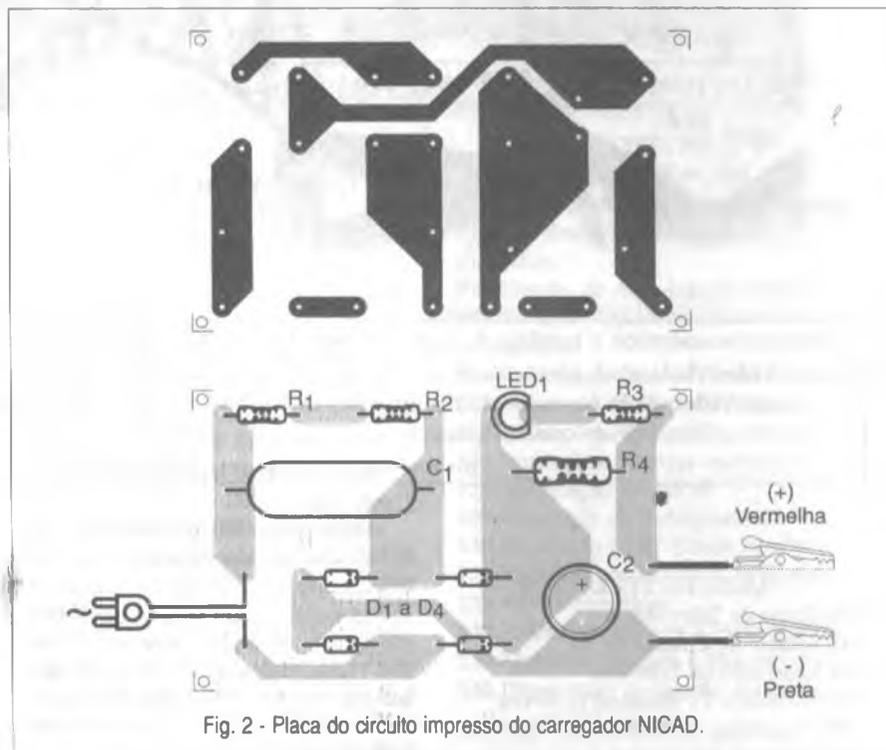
Placa do circuito impresso do carregador NICAD.
